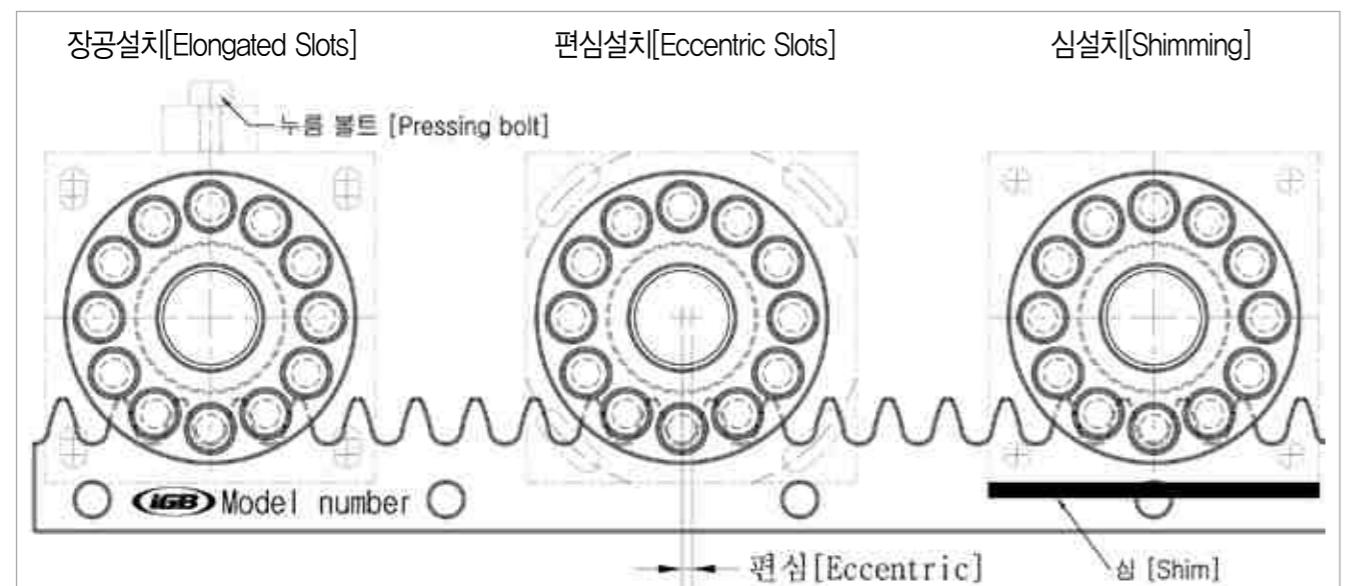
조립거리 조절이 가능한 피니언 설치 예 [Figure 10. Pinion installation examples for teeth engagement adjustment]
